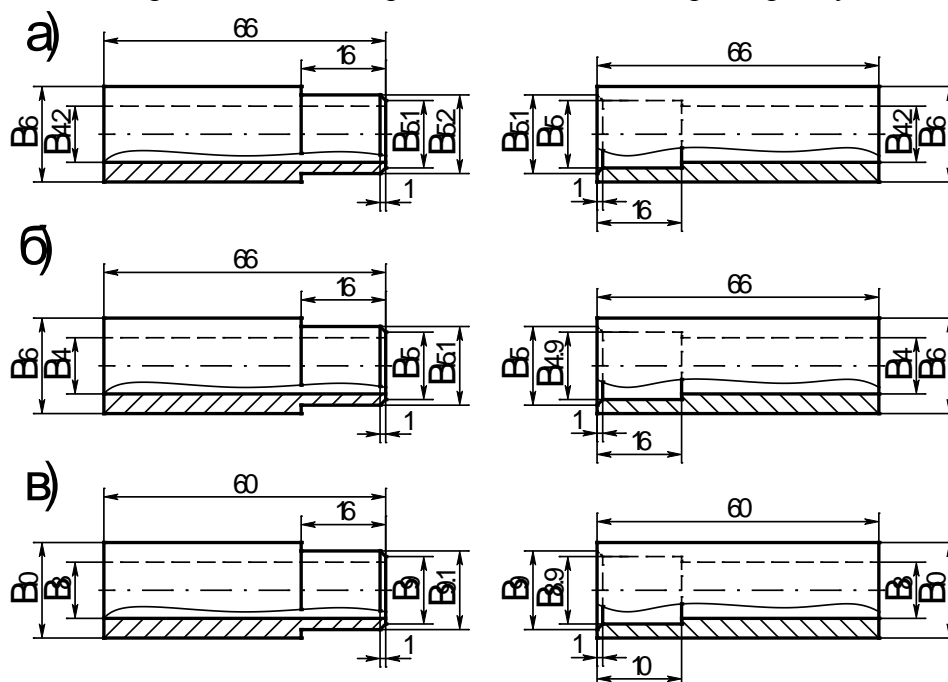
Эскизы заготовок для тугой посадки с натягом 100 микрон:
